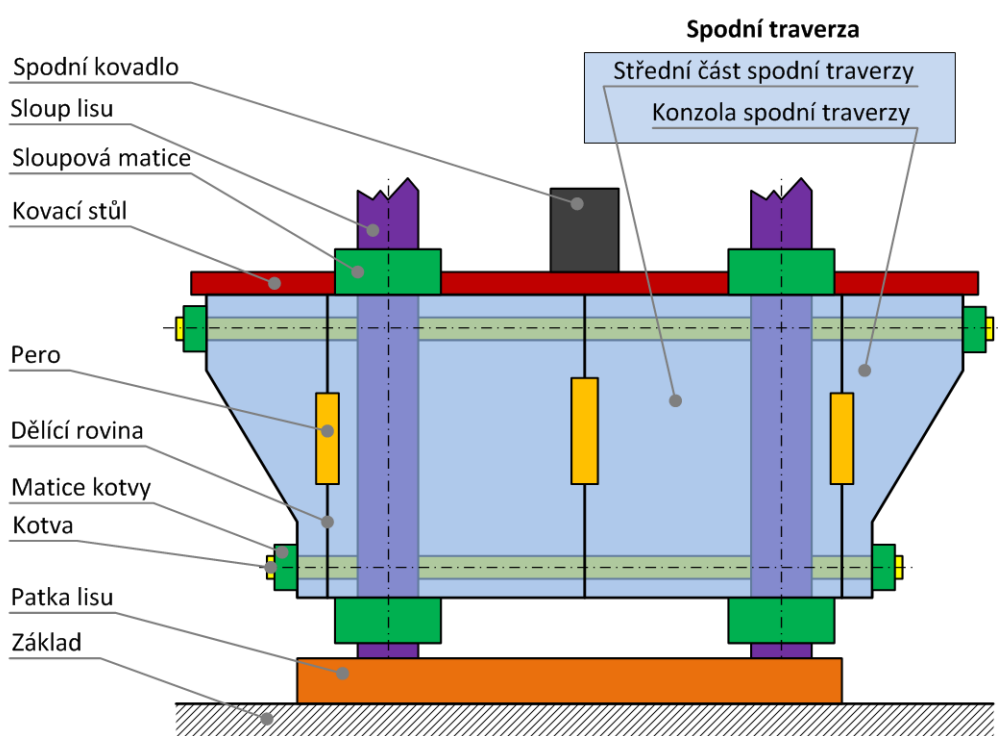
Dělená spodní traverza lisu CKV120/140MN
